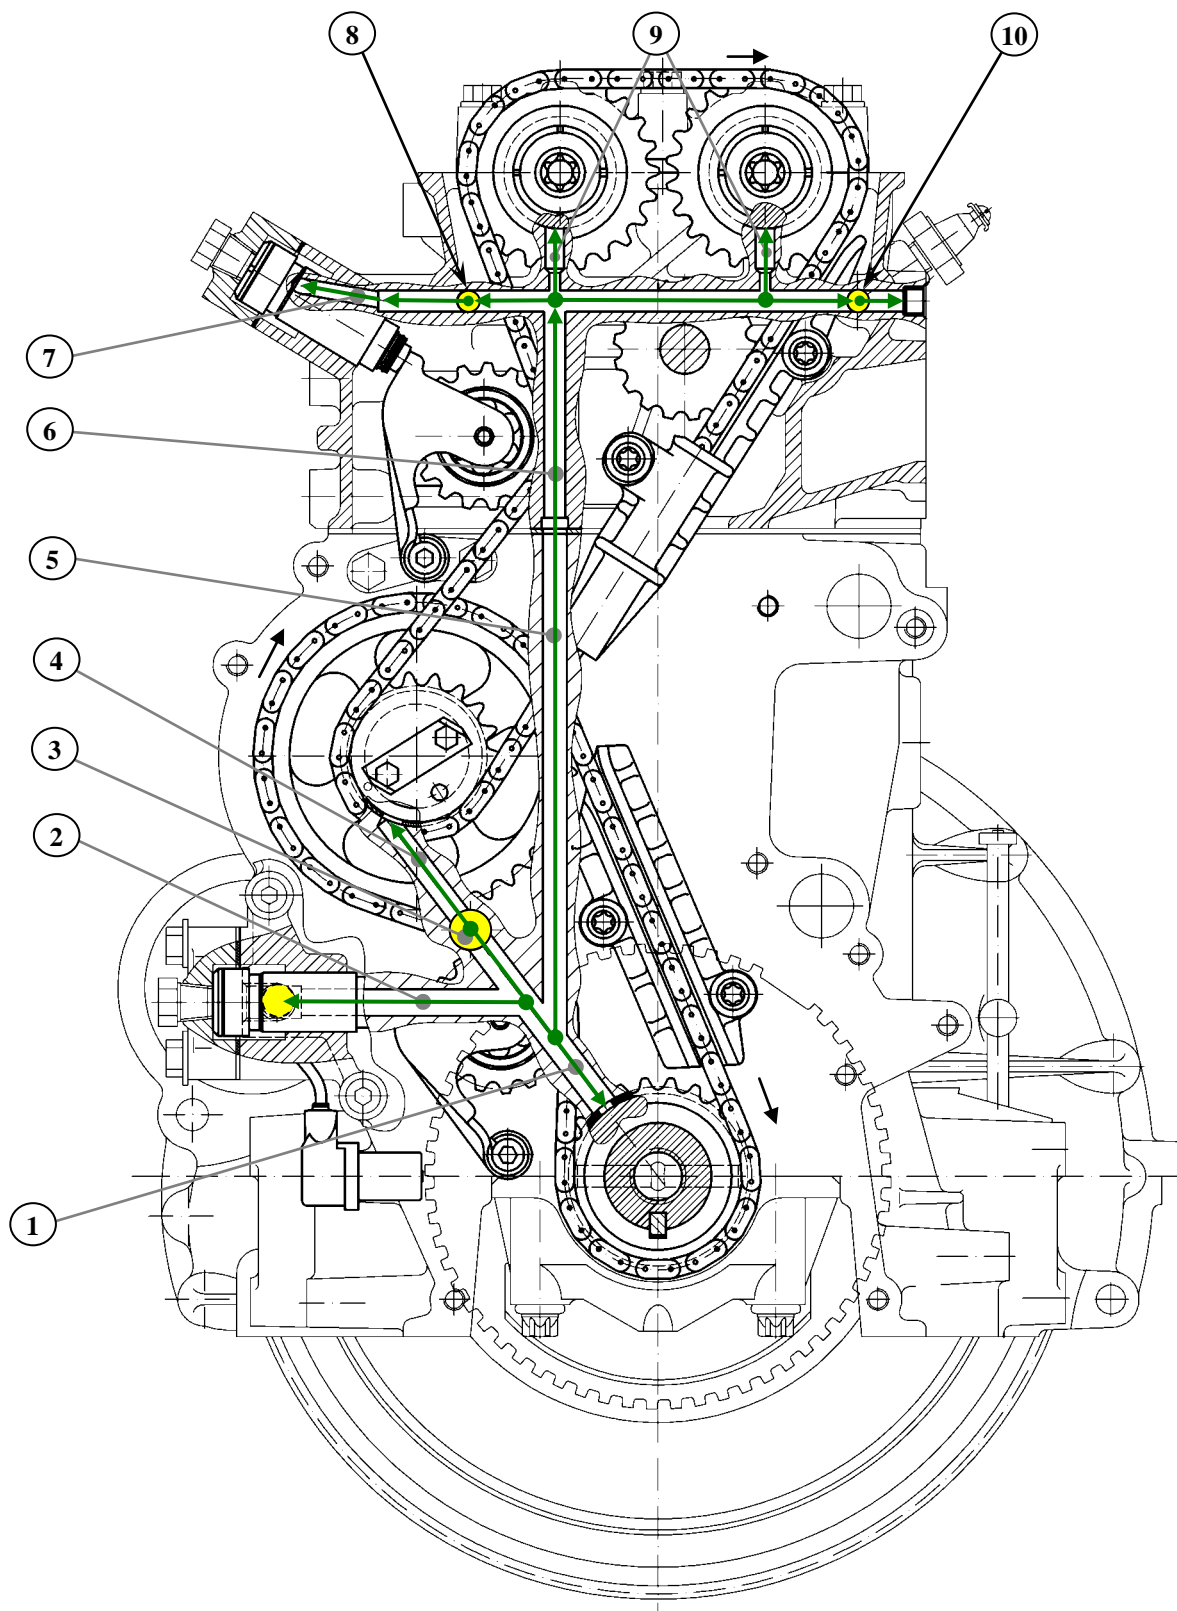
Схема циркуляции смазочного масла в двигателе:
